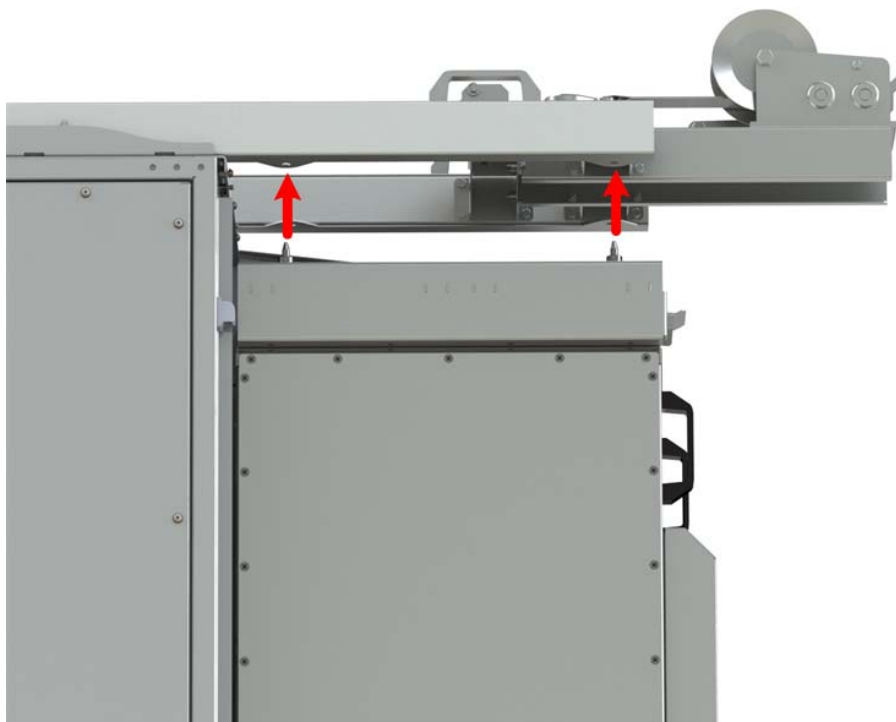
Стыковка каретки ячейки и подъемного механизма
